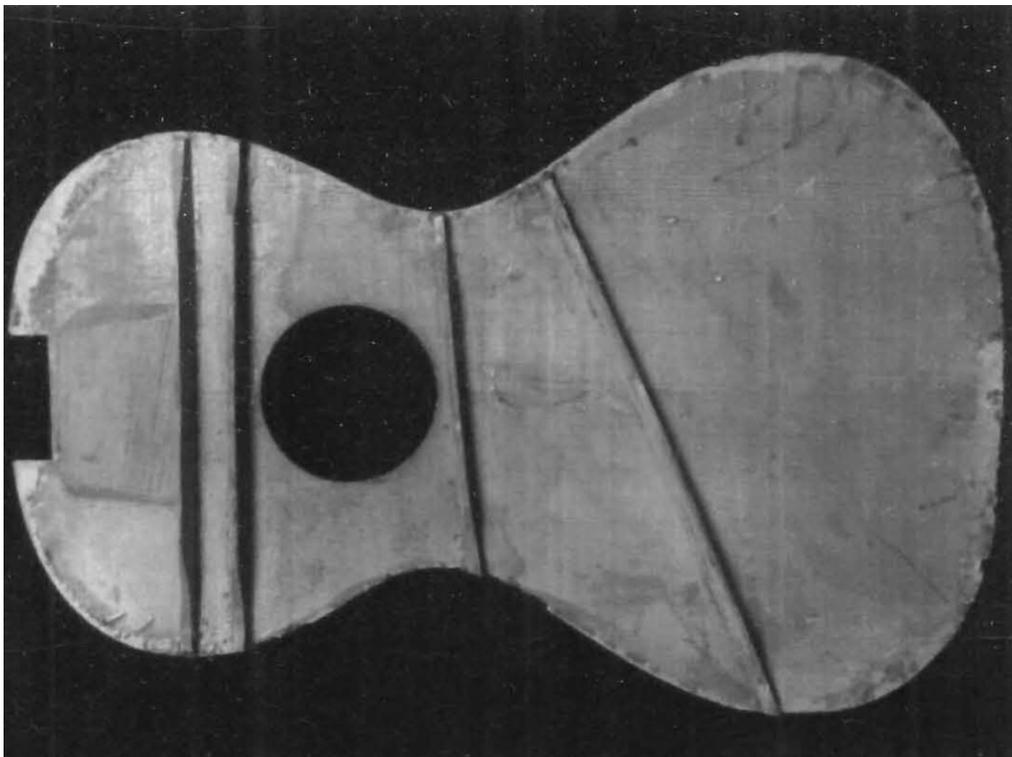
Innenansicht Decke G. B. Fabricatore 1806
